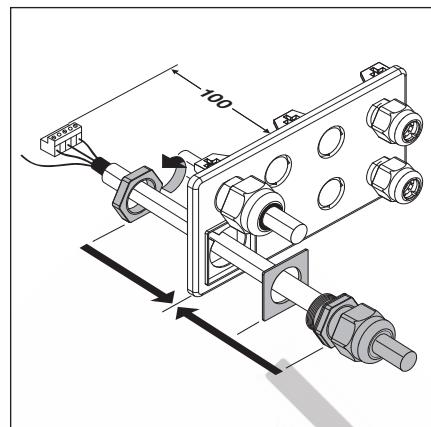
Endmontage der Verschraubungsflanschplatte
